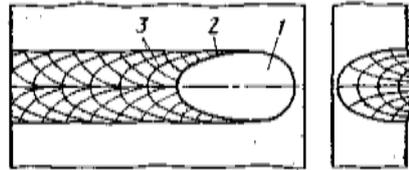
Столбчатые кристаллиты в сварном шве.
